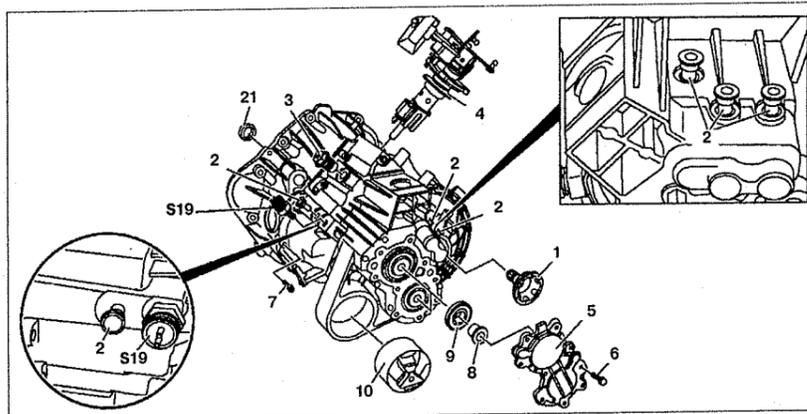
Разборка и сборка коробки передач (автомобили с двигателем 611.980):
